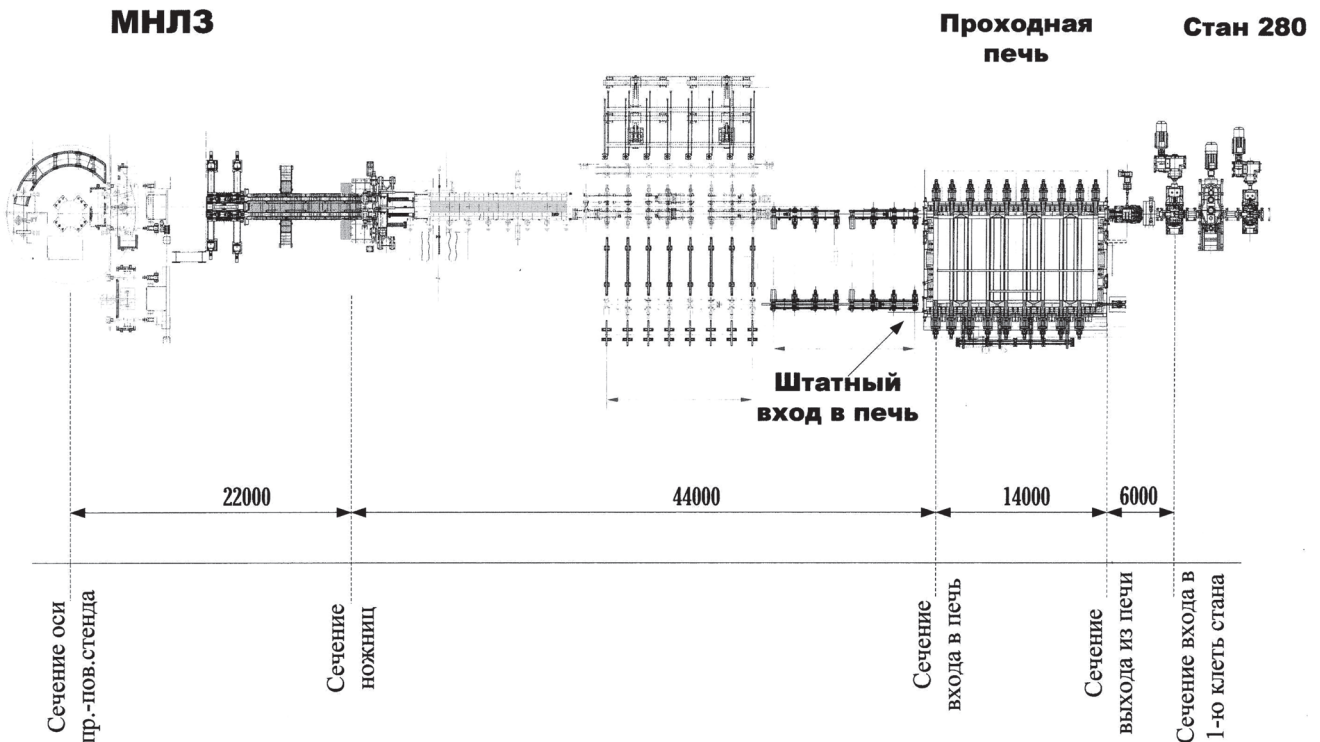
Участок продвижения металла от МНЛЗ до выдачи нагретой заготовки на прокатный стан 280
